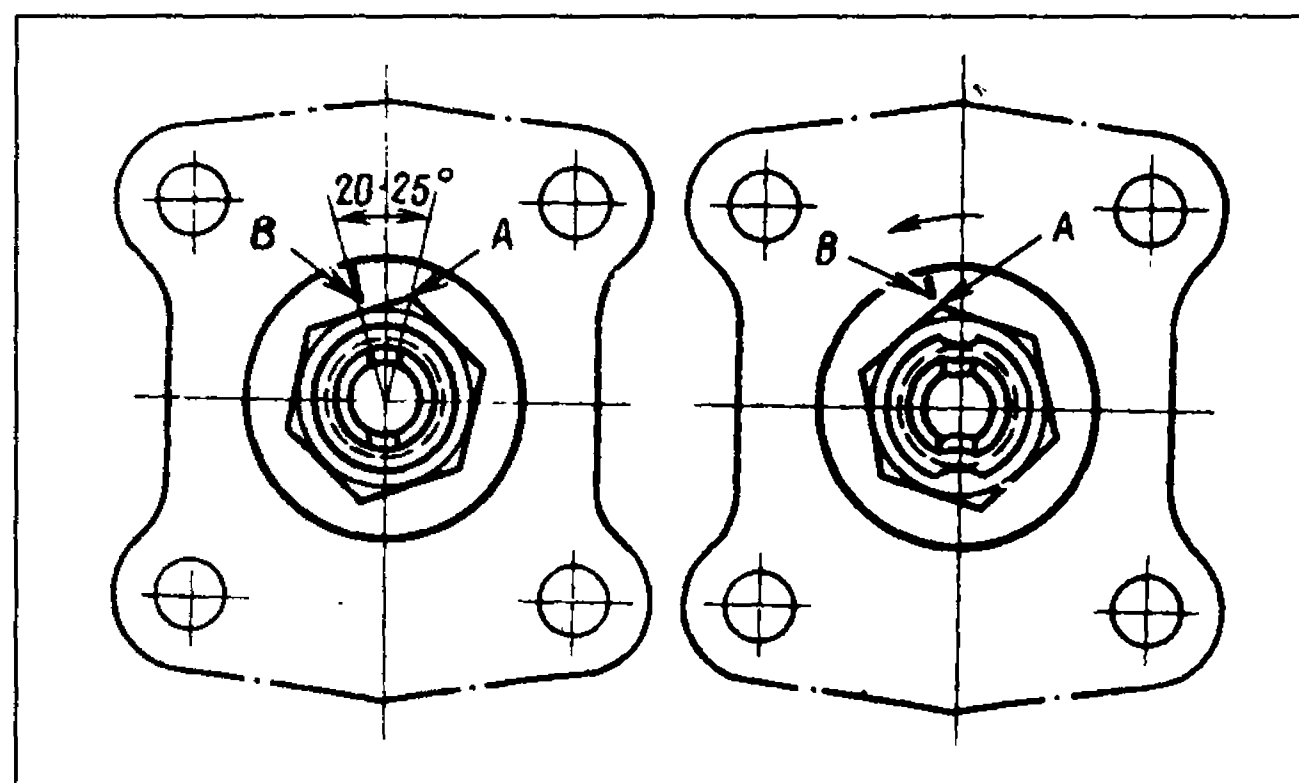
Схема регулировки подшипников ступиц передних колес: А-кромка гайки; В-метка на шайбе. Момент затягивания гайки 0,7 кгс·м. Ослабление гайки на 20-25°
